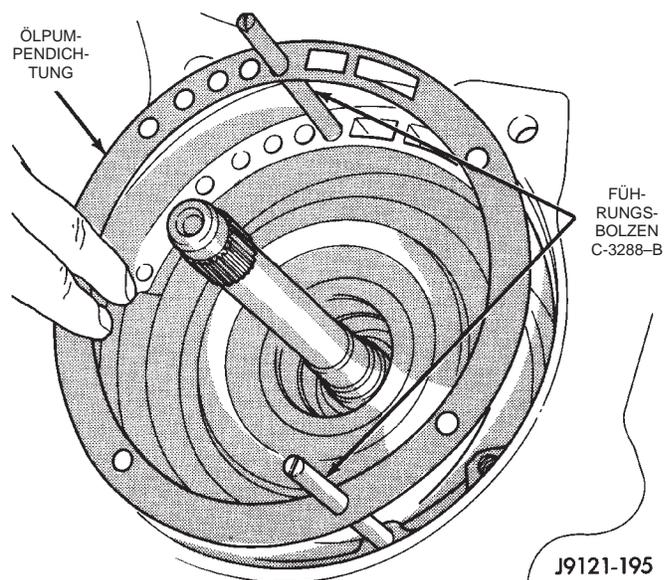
Führungsbolzen und Ölpumpendichtung montieren
